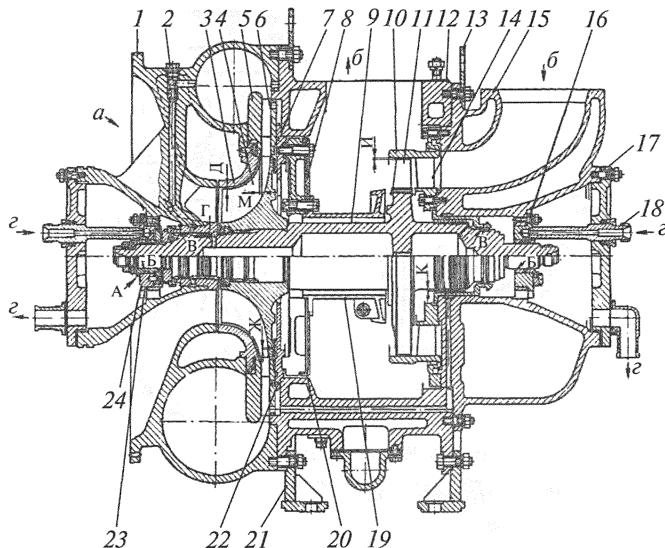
Продольный разрез турбокомпрессора ТК30Н:
